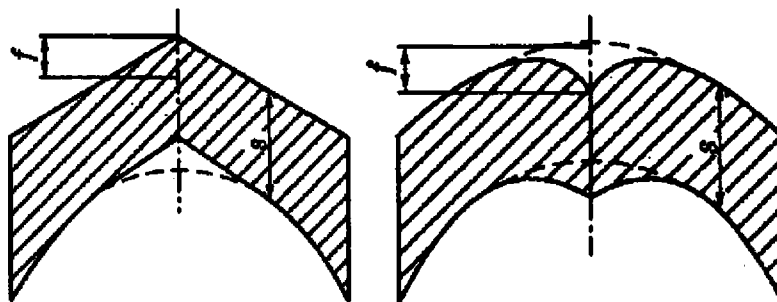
Увод (угловатость) кромок в сварных швах
